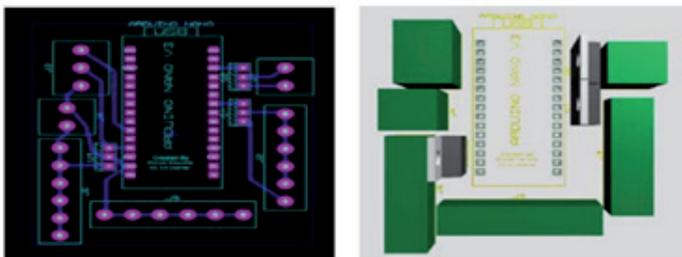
Diseño del PCB. Fuente: Elaboración propia
